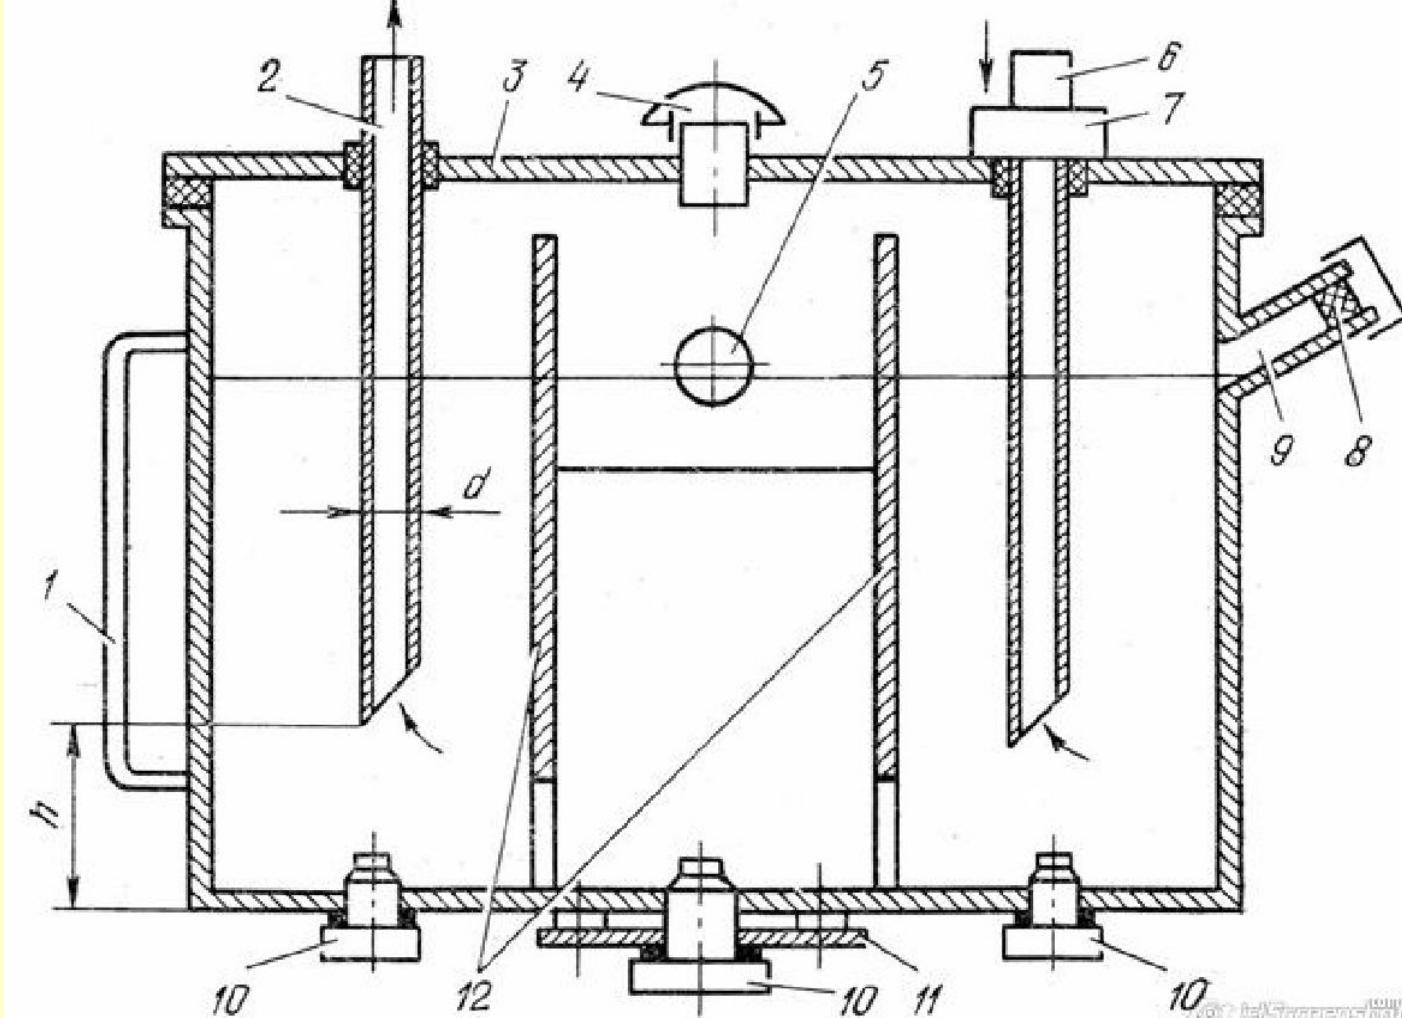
Гидробак: 1 - указатель масла; 2 - всасывающая труба; 3 - крышка; 4 - сапун; 5 - глазок; 6 - сливная труба; 7 - фильтр; 8 - сетчатый фильтр; 9 - заливное отверстие; 10 - пробка; 11 - крышка для слива РЖ; 12 - перегородки (успокоители)
